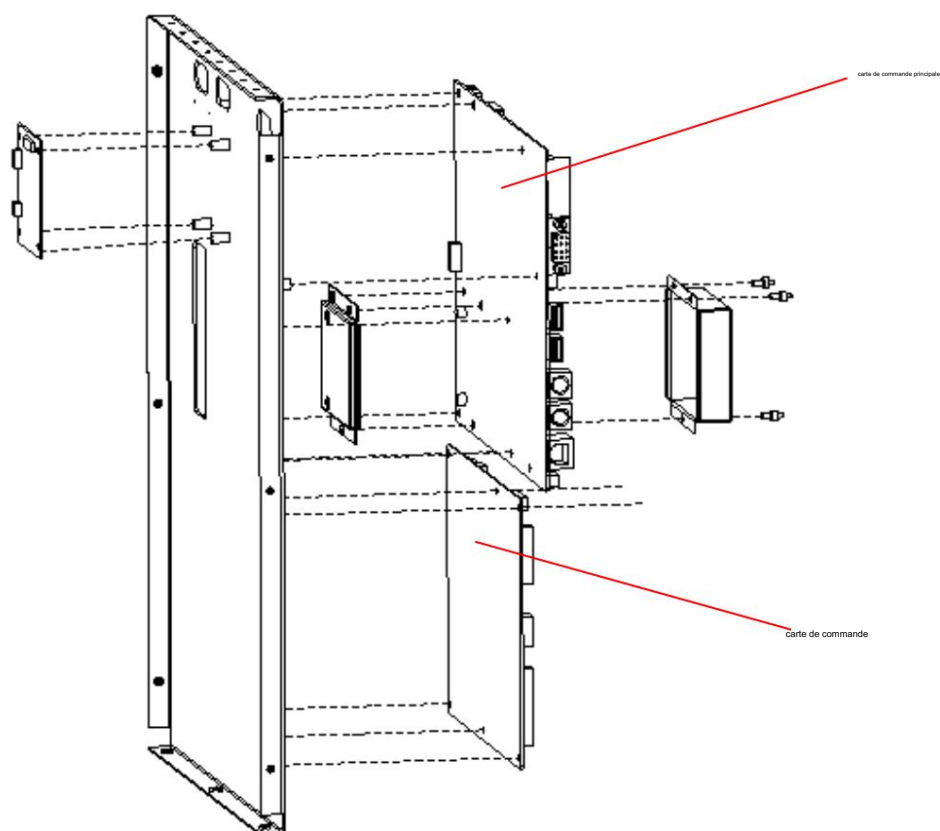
Démontage de la carte de commande principale et de la carte CPU
